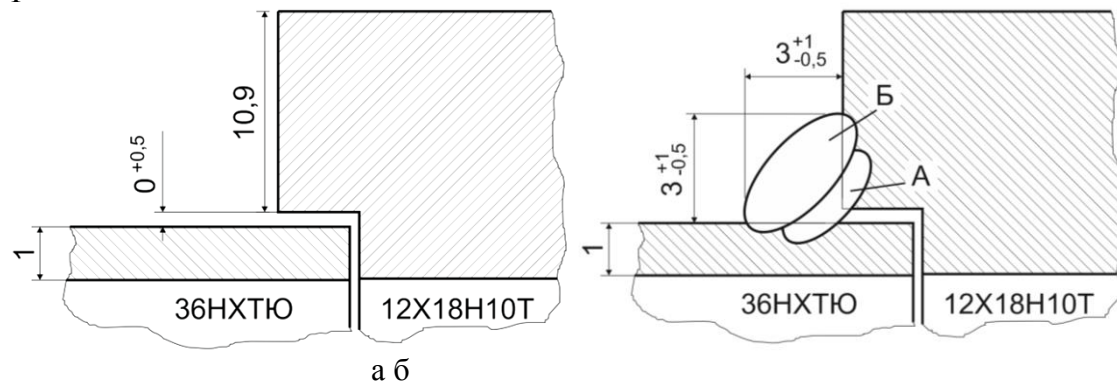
Схема выполнения сварных соединений из сплава 36НХТЮ и стали 12Х18Н10Т: а – форма разделки кромок, б – количество слоев и размеры сварного шва.
